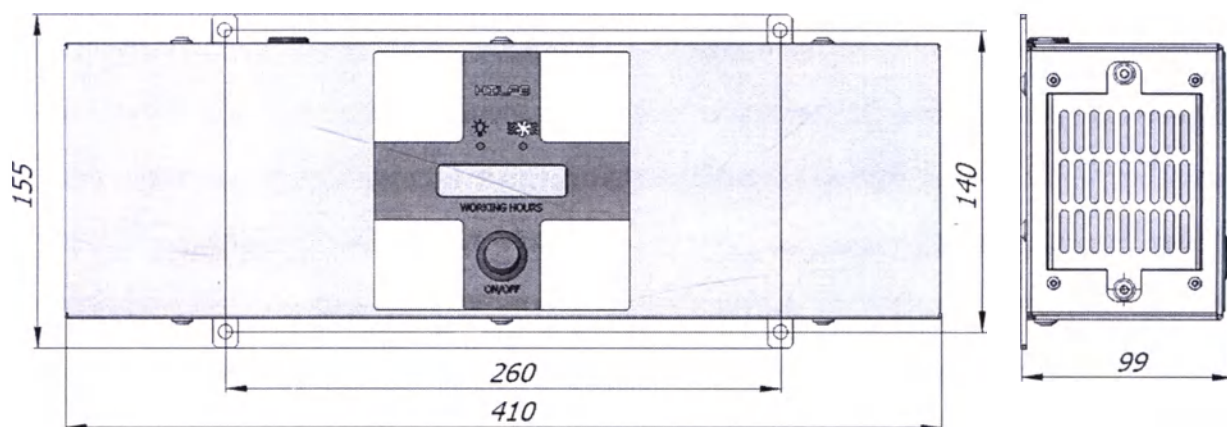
габаритные и присоединительные размеры рециркулятора
